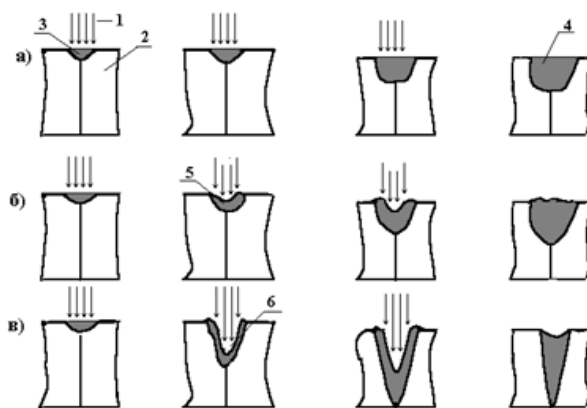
Стадии проплавки соединяемых деталей: 1 – лазерное излучение; 2 – детали; 3 – расплав; 4 – сварочная ванна; 5 – заглубление; 6 – отверстие, образованное вследствие перехода расплава в газообразную фазу; а – 10^5 – 10^6 Вт/см², б – $5 \cdot 10^5$ – $5 \cdot 10^6$ Вт/см², в – 10^6 – 10^7 Вт/см²
